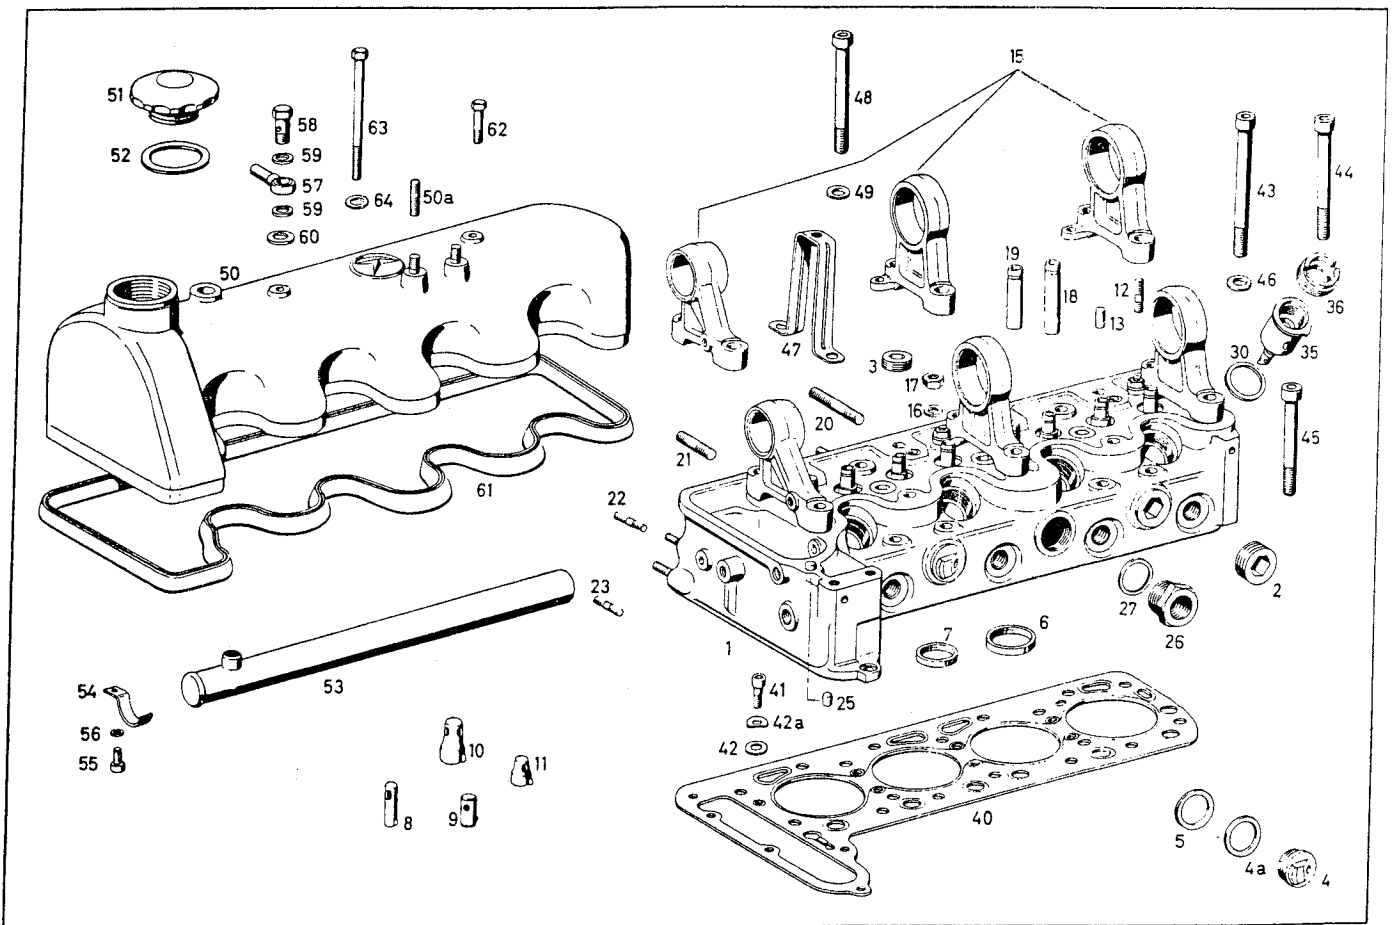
Montagebild des zerlegten Zylinderkopfes (OM 621)
